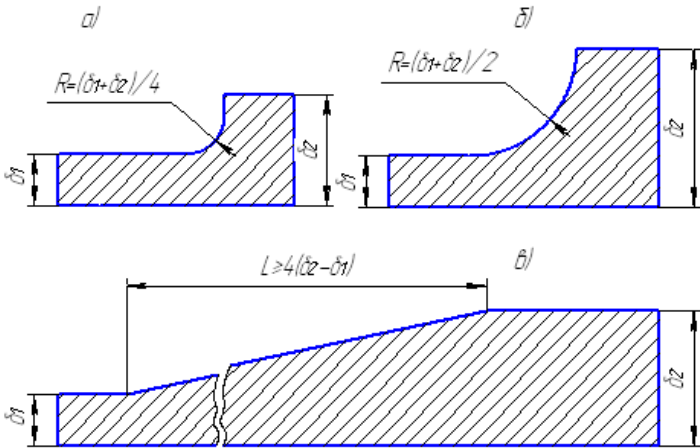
З'єднання стінок виливка різної товщини
